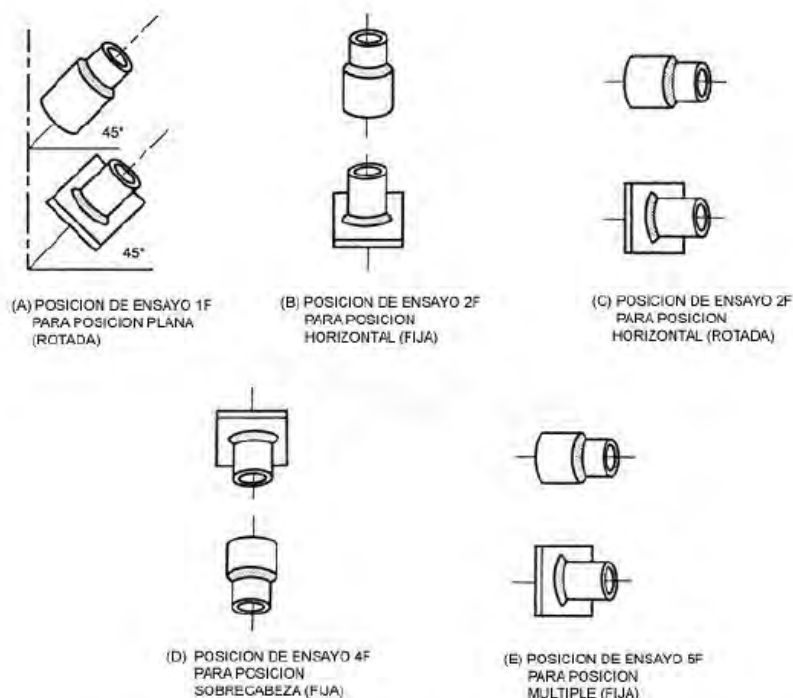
Posiciones de Tubos o Entubados de Ensayos para Soldaduras de Filete (ver 4.2.4)
